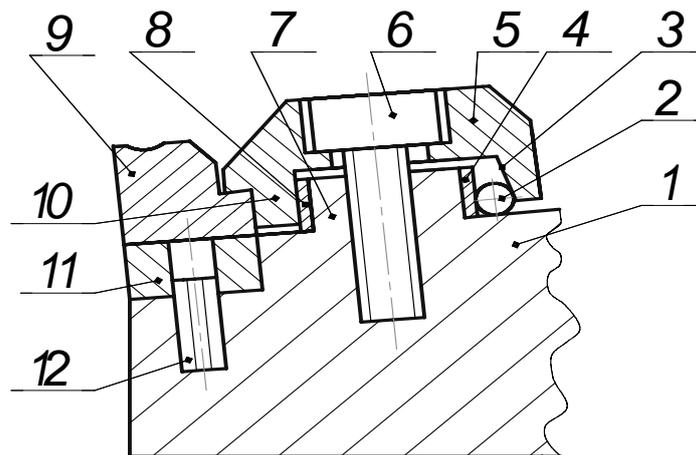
Сборный резец по авторскому свидетельству № 1232384 (конструкция 4)
